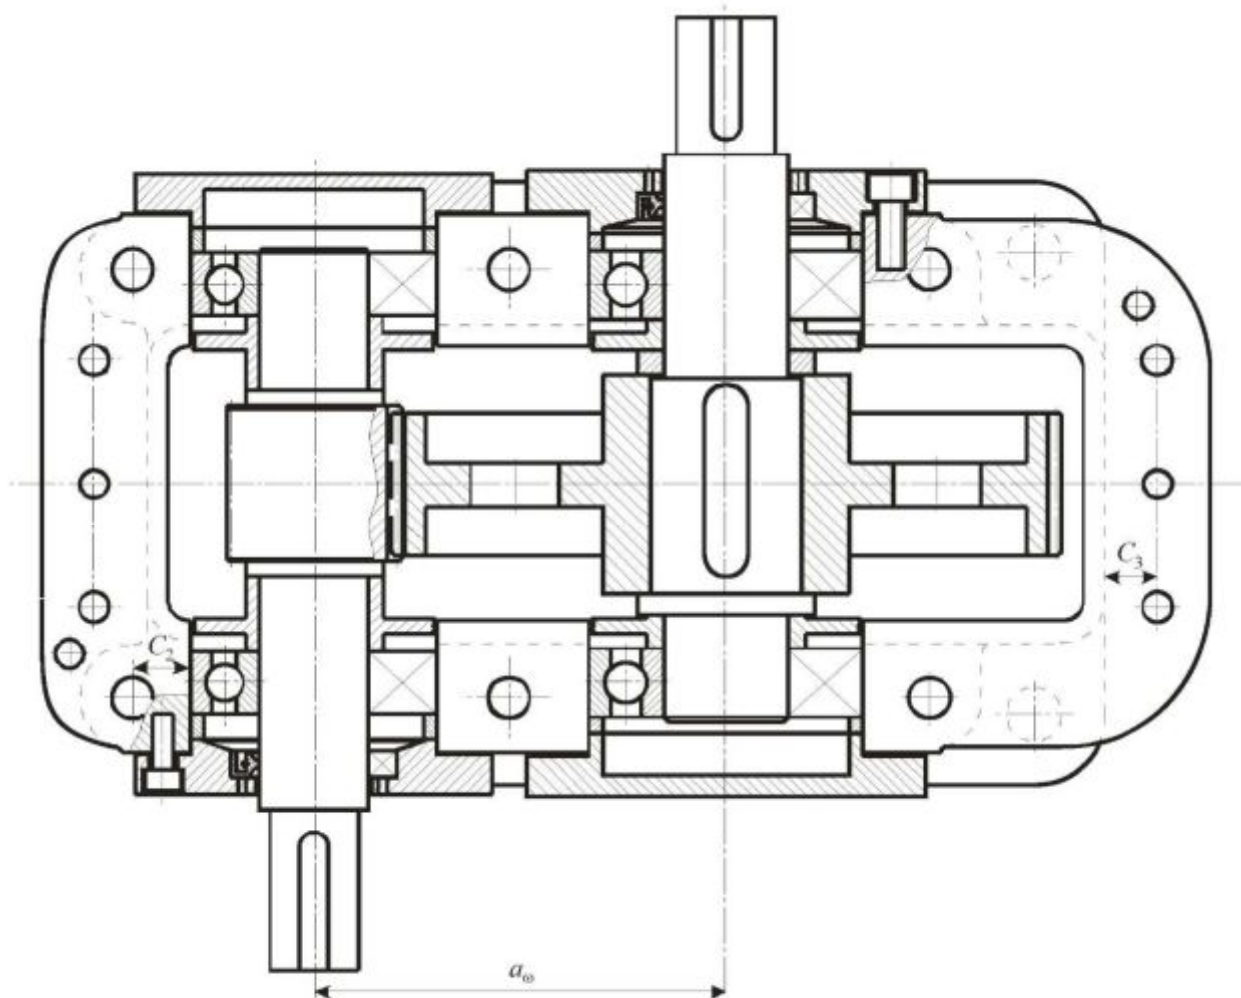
Оформление подшипниковых крышек, валов и отверстий под болты
